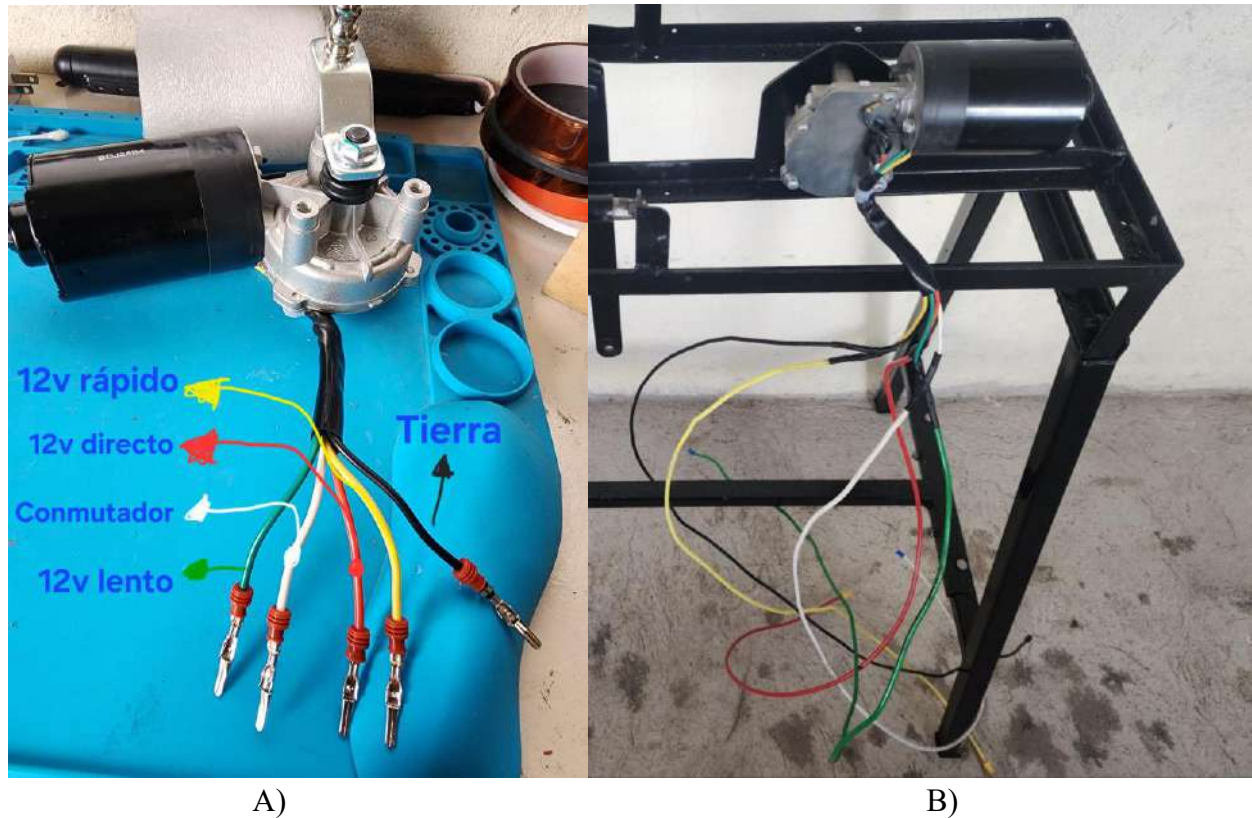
A) Identificación de los cables del motor, B) Extensión de cables
